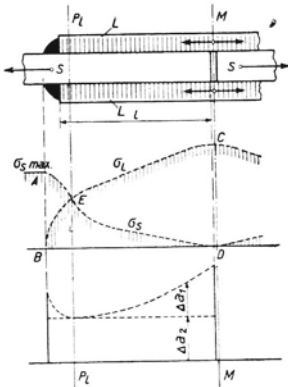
Stab mit Fuge; das Flacheisen ist in Stirn- und Flankennähten angeschweißt.
